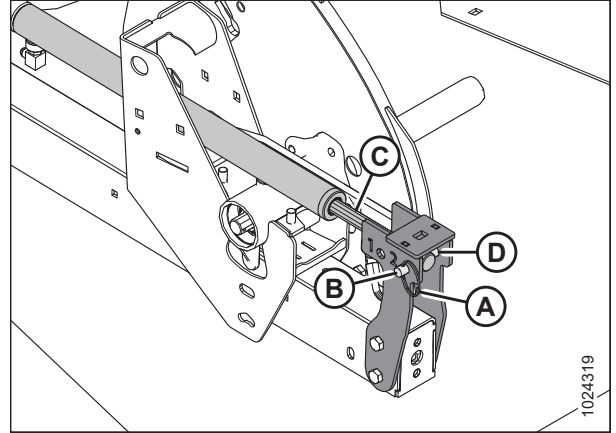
Циліндр правого важеля мотовила в передньому положенні
